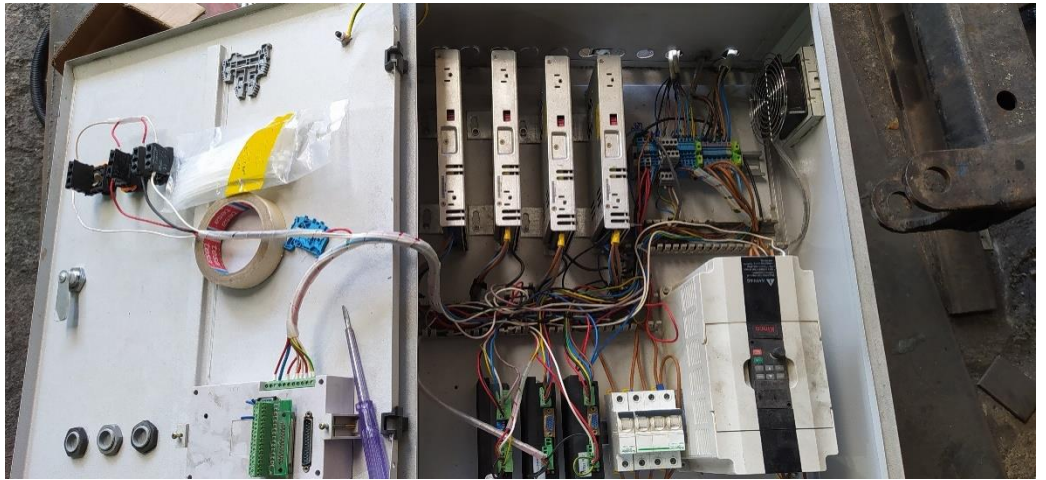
CNC Router Mekanik Kısım Son Montajı-3
